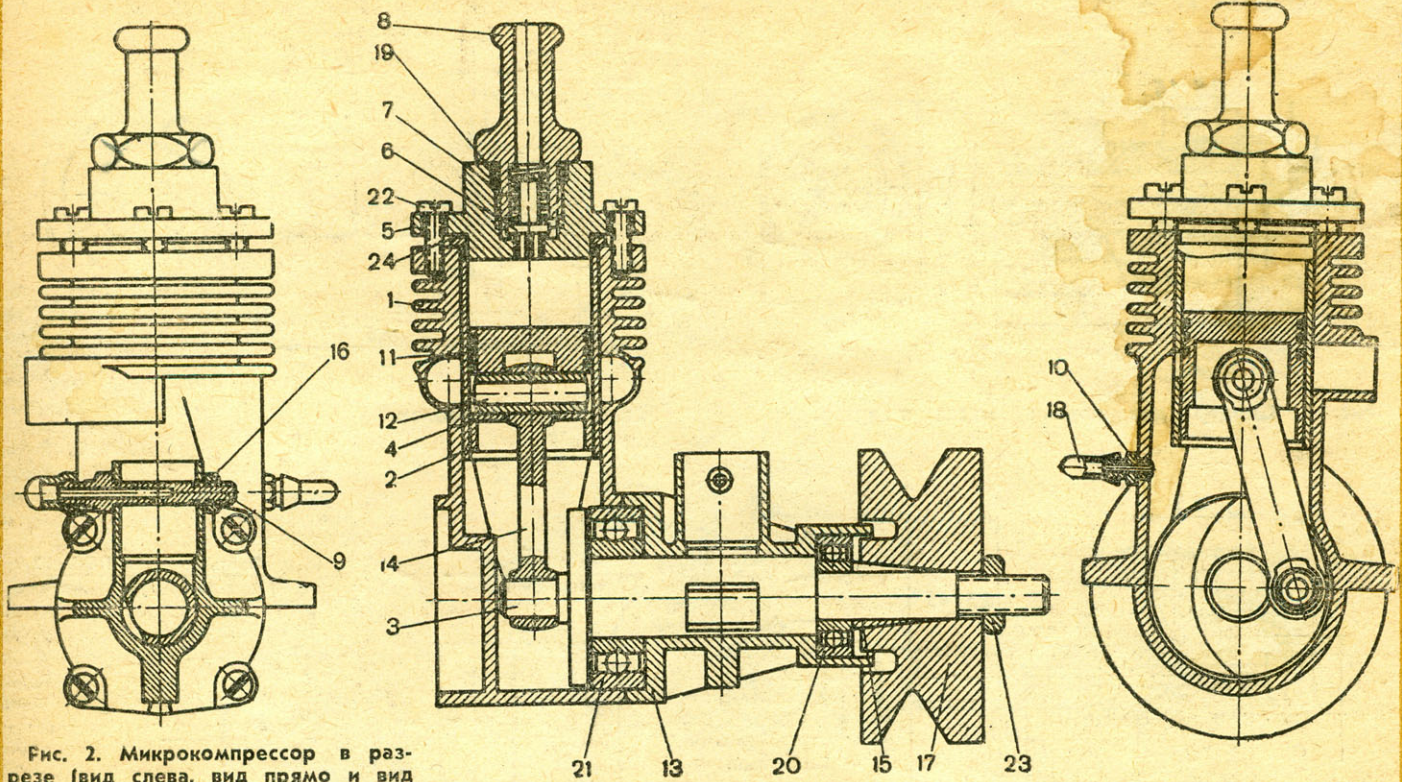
Микрокомпрессор в разрезе (вид слева, вид прямо и вид справа):
